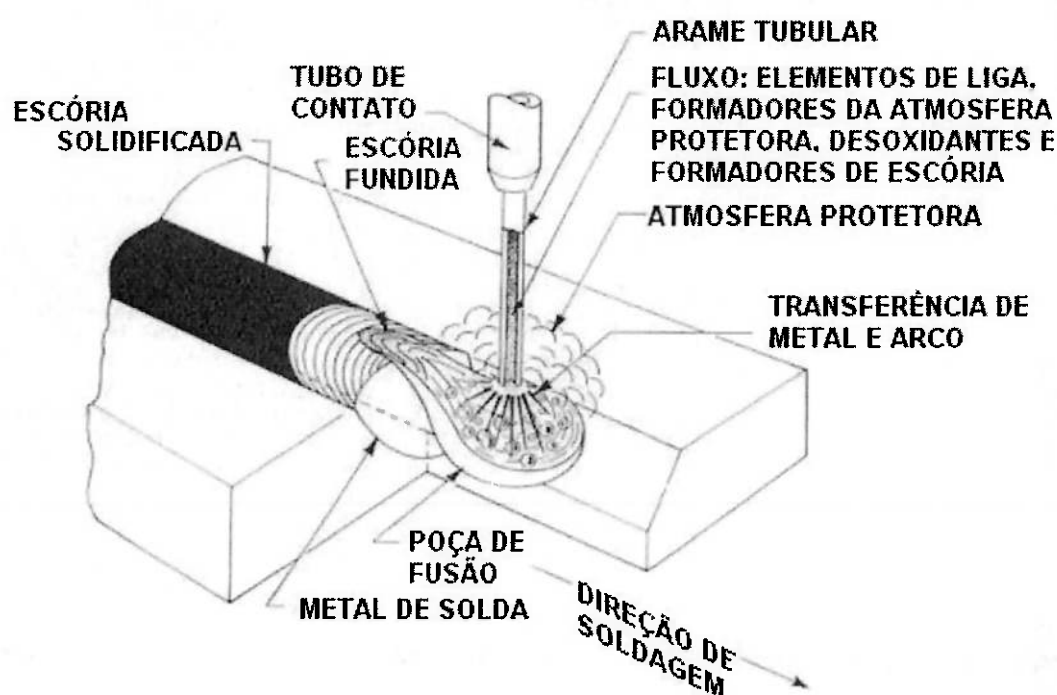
12 - Processo de soldagem com arame tubular autoprotegido. [7]
